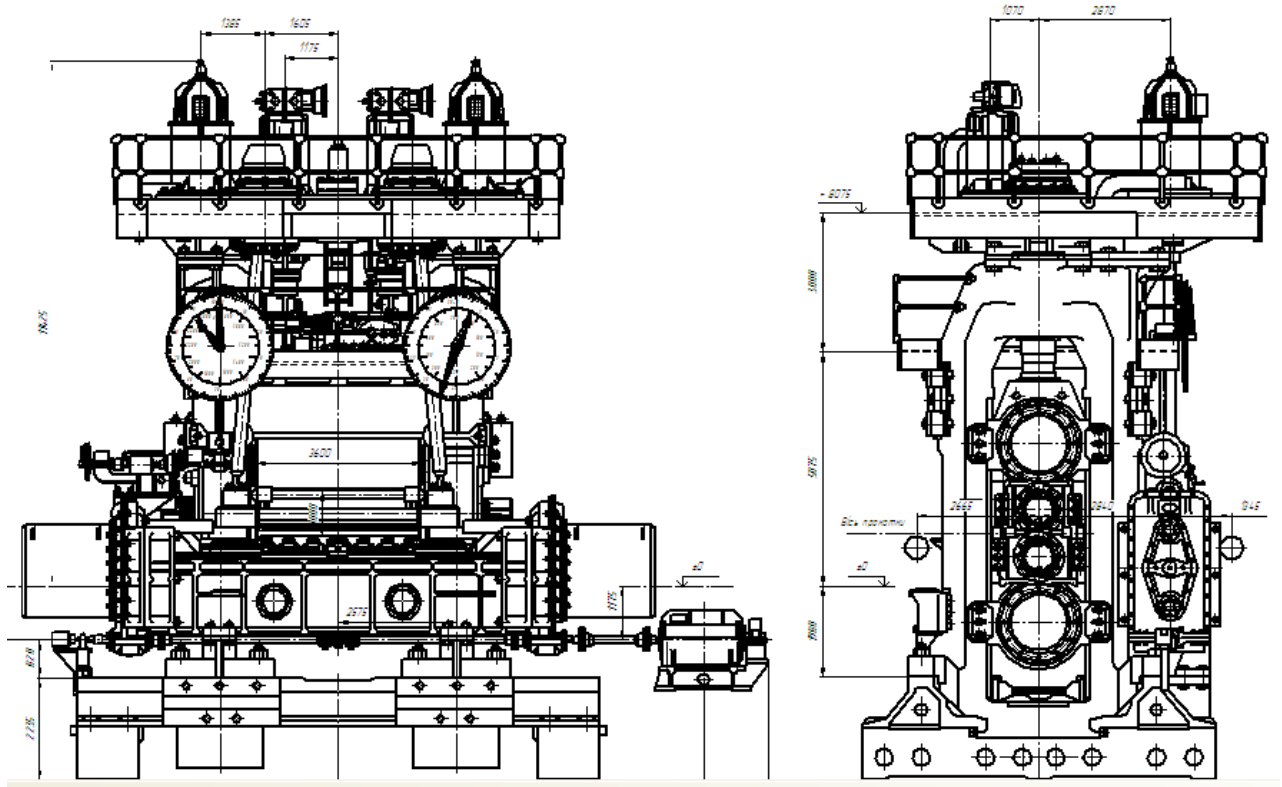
Загальний вид чорнової реверсивної кліть кварто 1130/1800x3600
